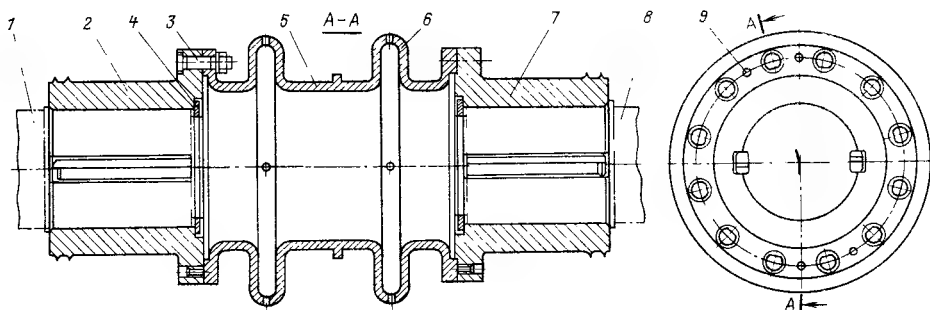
Конструкция полужесткой муфты ЛМЗ:
